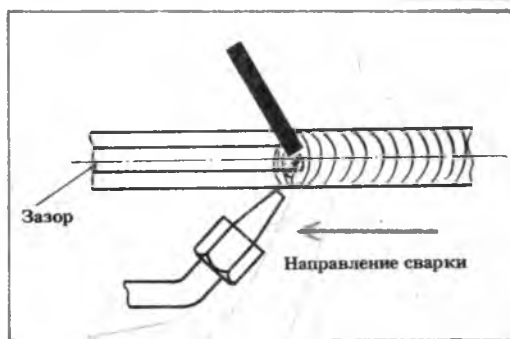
Сварка сквозным (двойным) валиком
